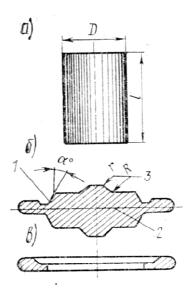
Схема изготовления поковки путем горячего деформирования:
